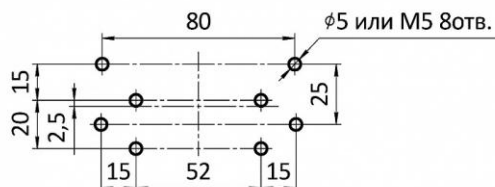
Габаритные и установочные размеры передающего преобразователя
